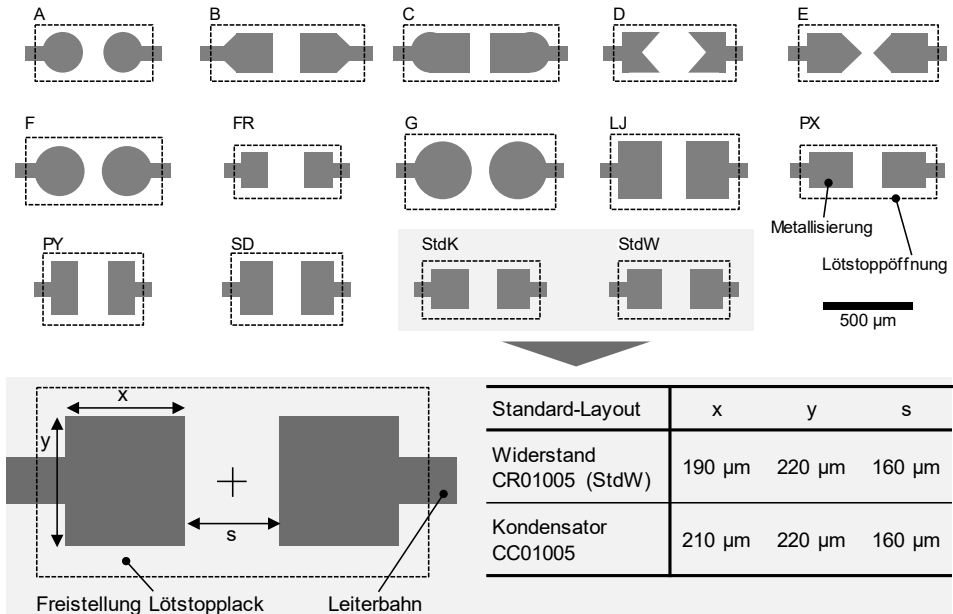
Layoutvarianten und abgeleitetes Standard-Layout für die SMD-Landeflächen
